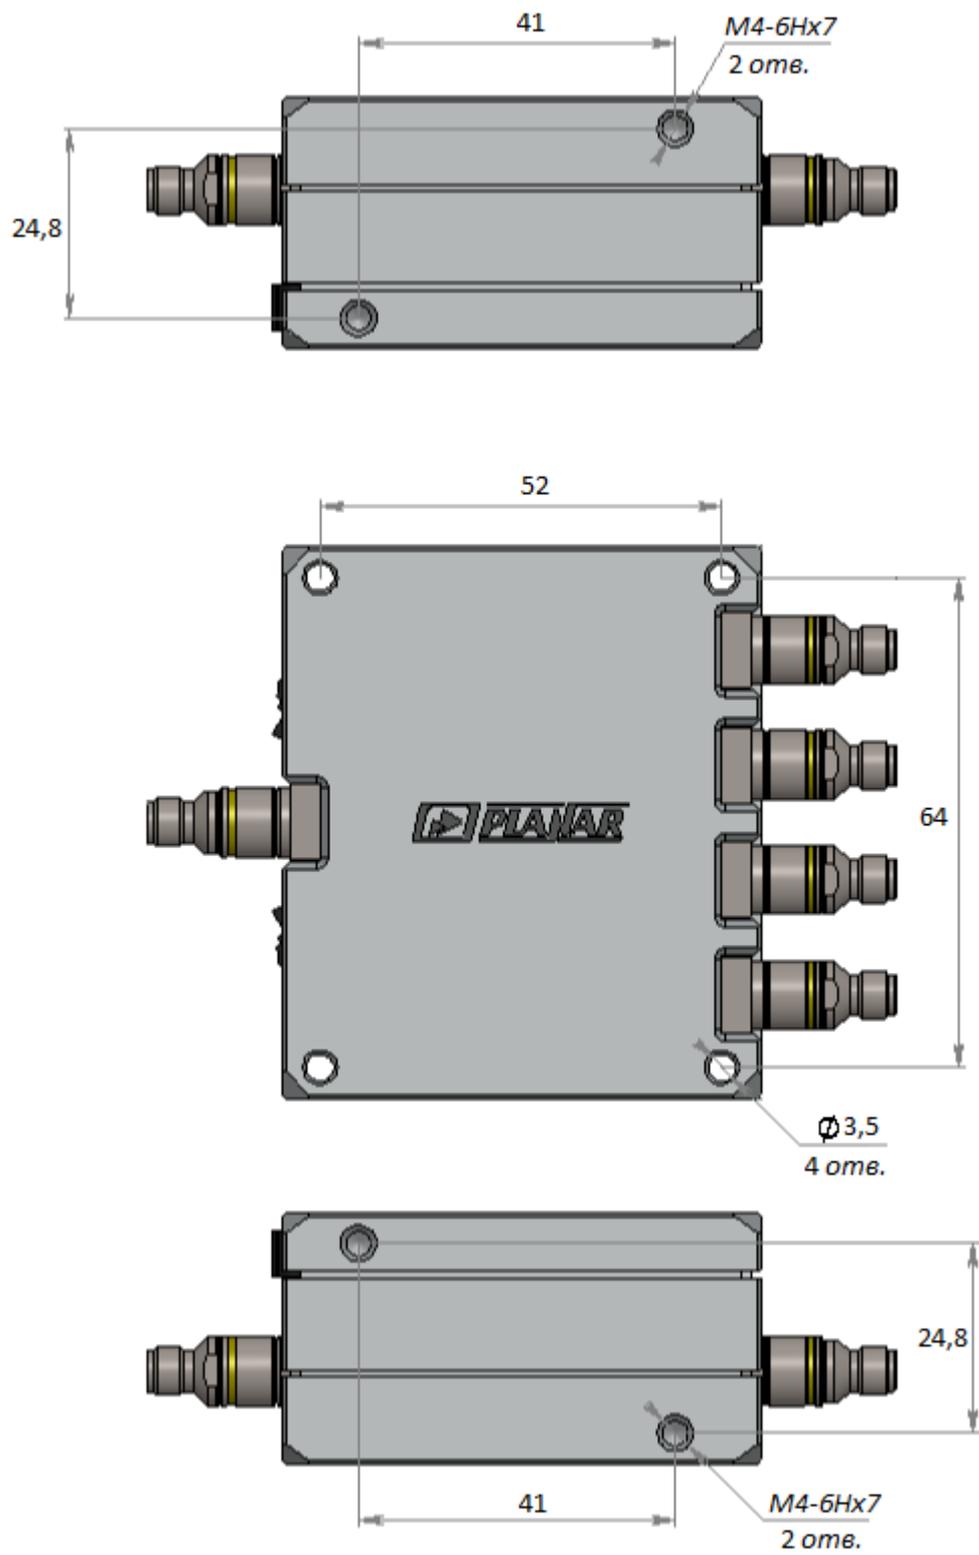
Расположение монтажных отверстий на лицевой и торцевых сторонах
